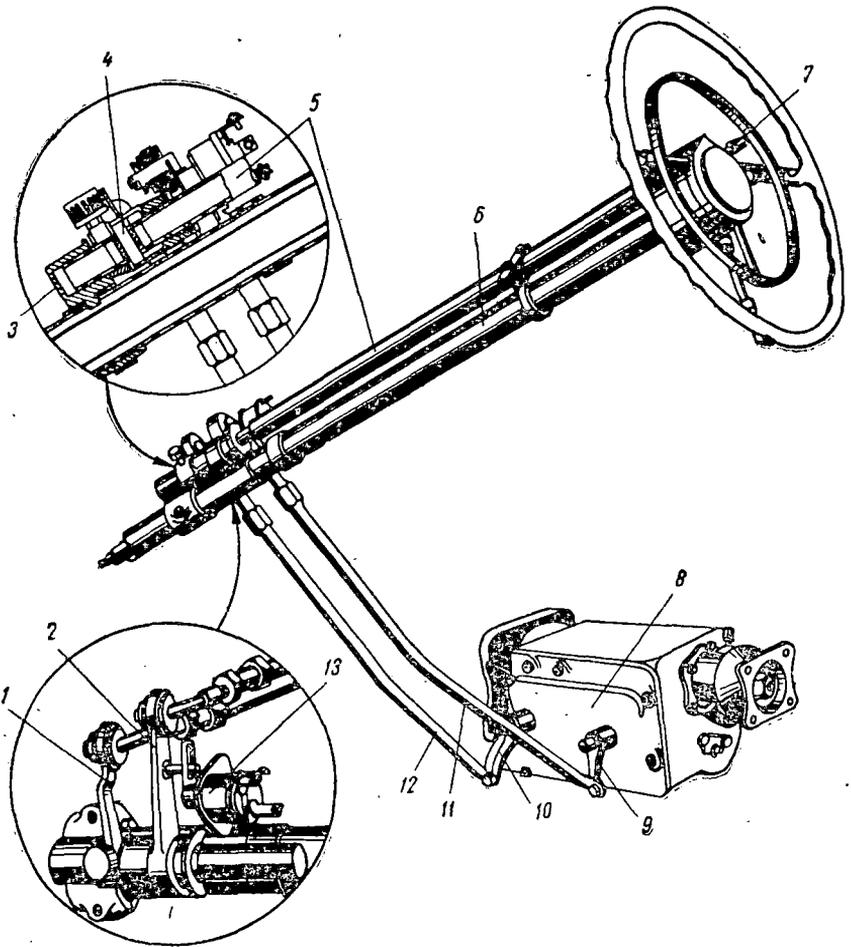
Механизм управления коробкой передач автомобиля ГАЗ-21 «Волга»: 1 и 2 — рычаги; 3 — нижний кронштейн; 4 — штифт; 5 — вал переключения; 6 — рулевая колонка; 7 — рычаг переключения; 8 — боковая крышка; 9 и 10 — рычаги; 11 и 12 — тяги переключения передач; 13 — включатель света заднего хода
